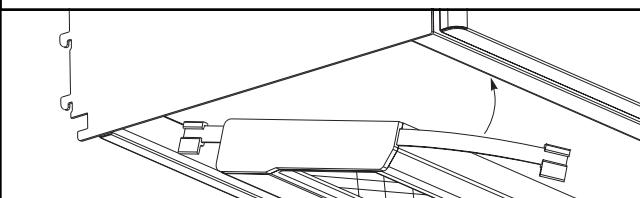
Assembler les glissières de montage et les pinces de réglage :
